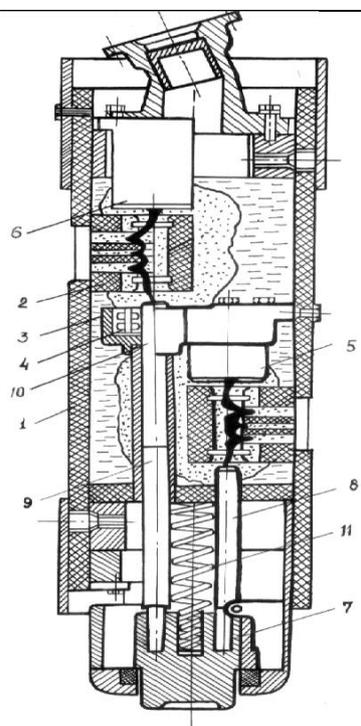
Дугогасительное устройство выключателя У-110
